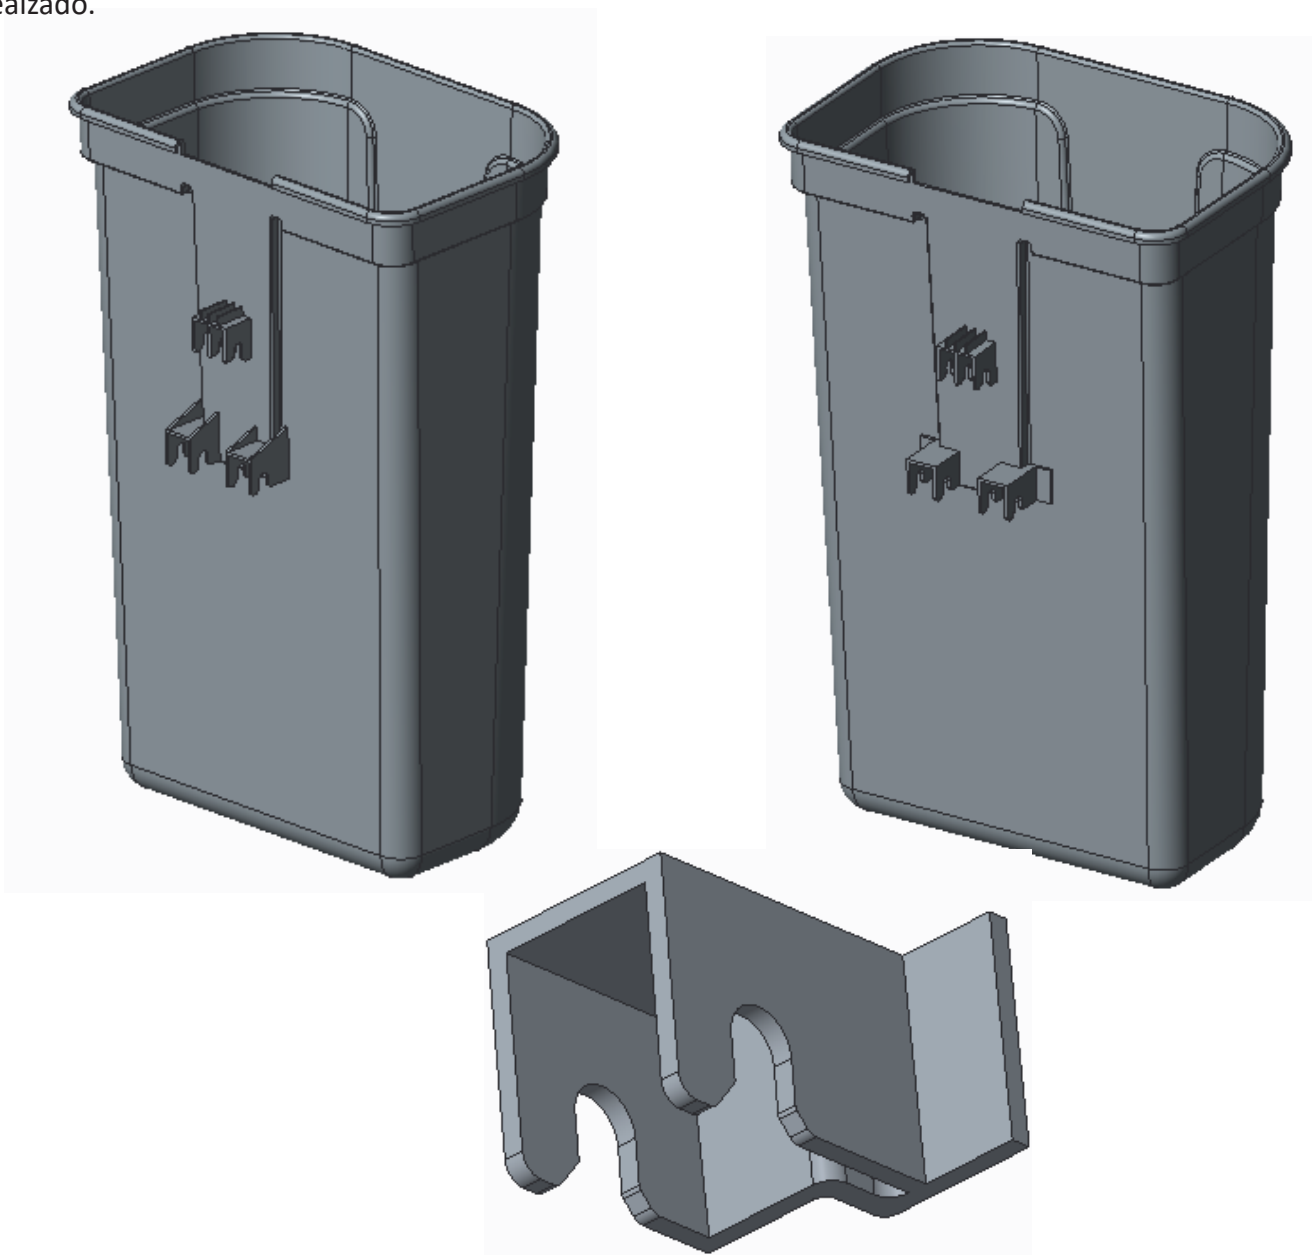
Vistas en tres dimensiones de la papelerera mostrando las dos opciones: izquierda, los enganches salen del molde; derecha, con pieza clipada. Abajo, se muestra la pieza clipada.
